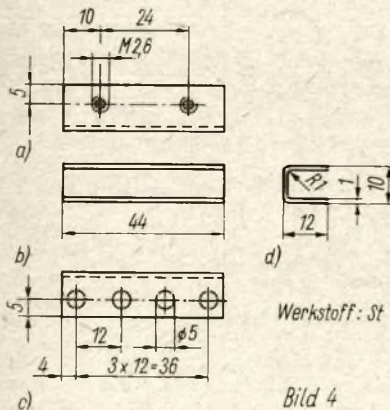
Maßskizze des Kühlblechs für 4 Stück Flächengleichrichter GY 110 (OY 110)
